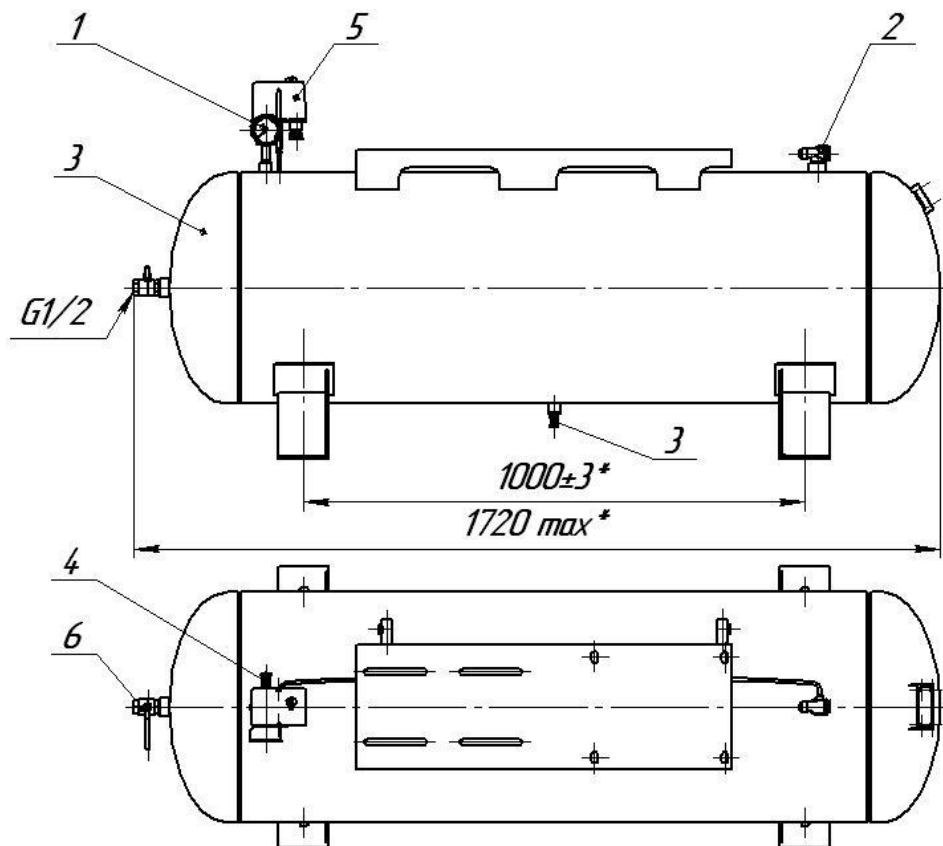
Ресивер установки компрессорной, модель К-20:
